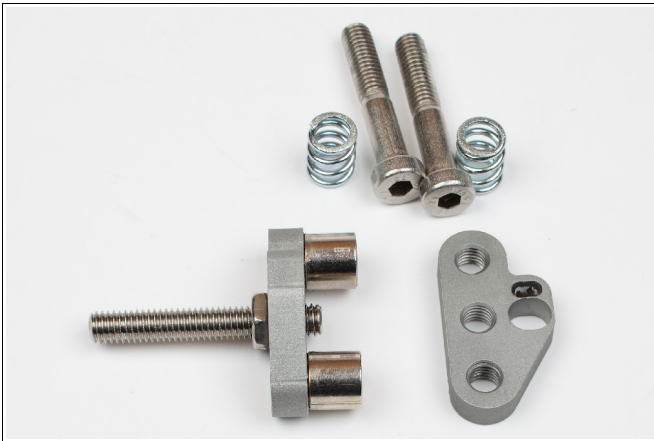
Beide Platten werden gedreht, wobei sowohl die Buchsen als auch die Magnetplatte mit dem Magneten nach innen zeigen. Anschließend wird die Madenschraube M6x40 befestigt.
